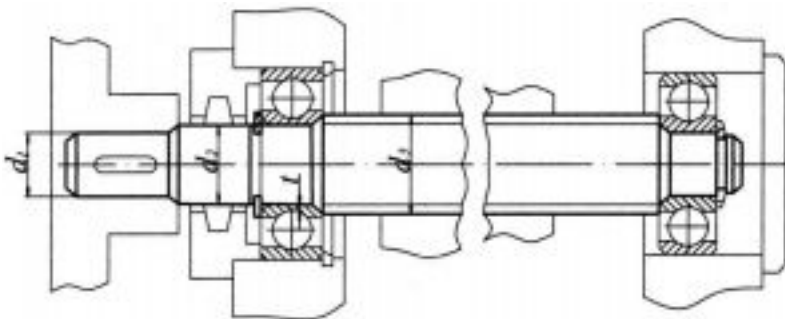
Конструкция входного (или выходного) шлицевого вала коробки передач
